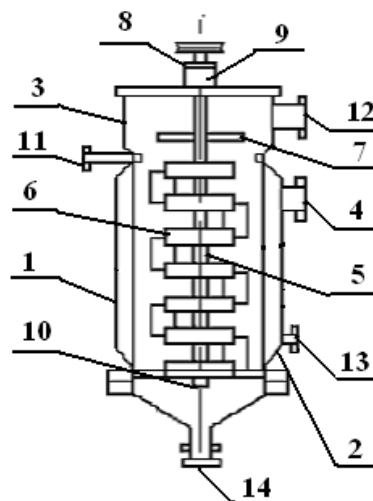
Лабораторний апарат 1-корпус; 2-сорочка для теплоносія; 3-сепаратор; 4-штуцер гріючої пари; 5-ротор; 6-лопатки; 7-відцентровий відбійник; 8-верхній підшипник; 9-сальник; 10-нижній підшипник; 11-штуцер для підведення продукту; 12-штуцер вторинної пари; 13-штуцер конденсату; 14-штуцер концентрату.
